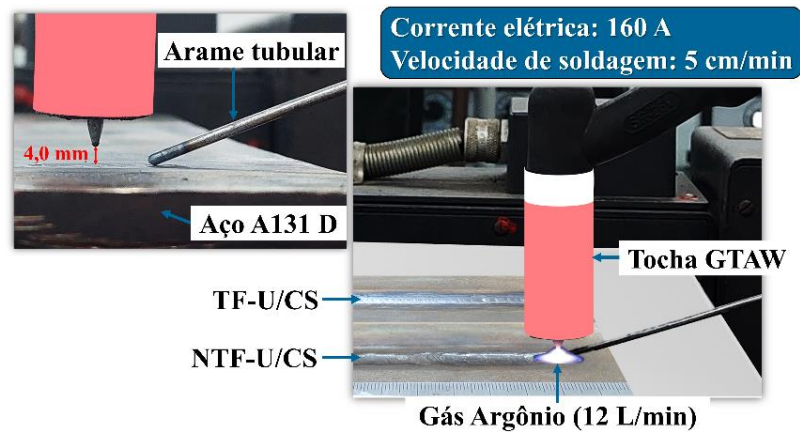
Ilustração esquemática do processo de soldagem via GTAW com adição de arame tubular.
